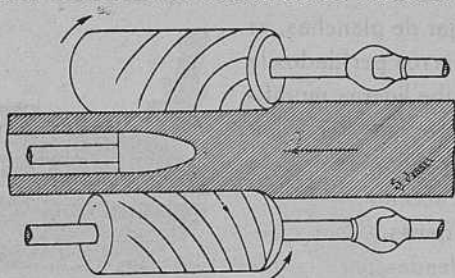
Procedimiento Mannesmann para fabricar tubos sin soldadura.
